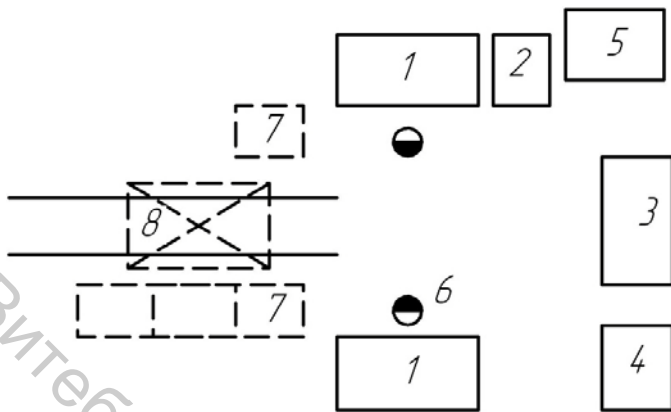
План рабочего места контролёра: 1 – стол контролёра ОТК; 2 – малая тележка; 3 – поверочная плита; 4 – инструментальная тумбочка; 5 – инструментальный шкаф; 6 – подъёмно-поворотный стул; 7 – приёмный стол рольганговой секции; 8 – каретка-оператор цехового транспорта для обслуживания рабочих мест механической обработки деталей
